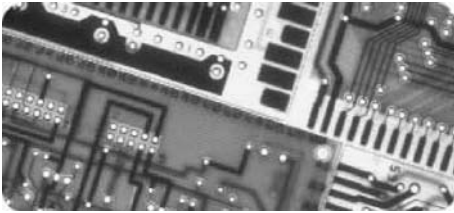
Bohren von Mikrovias in Printed Circuit Boards (PCBs) [15.9]
